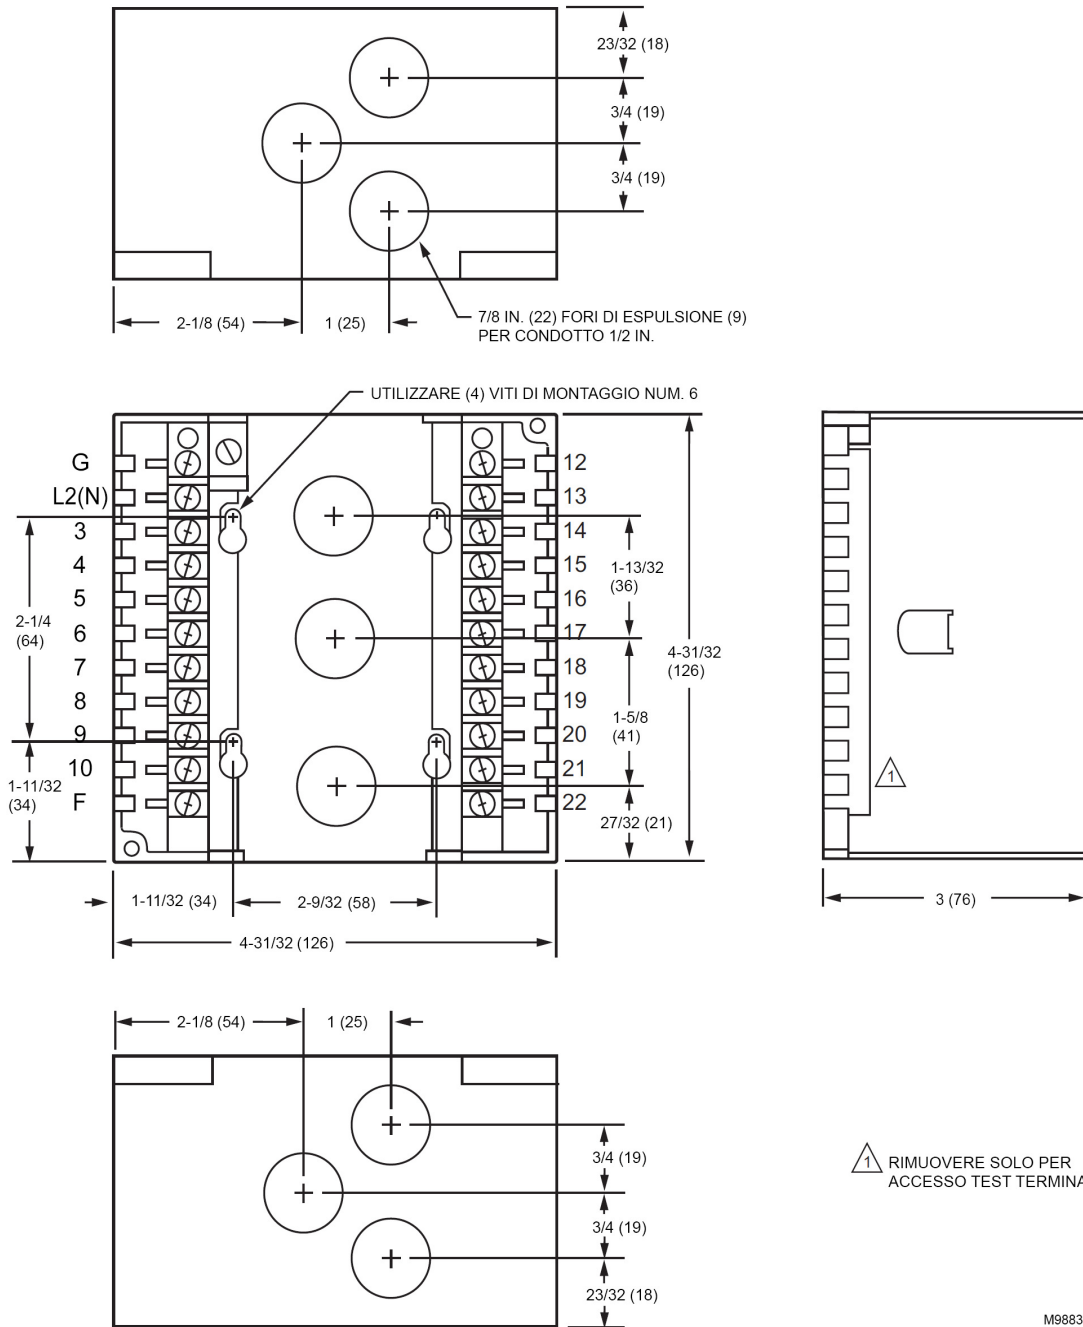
Vista superiore e frontale della sottobase di cablaggio Q7800B1011 (4 lati) con dimensioni in pollici (mm).
